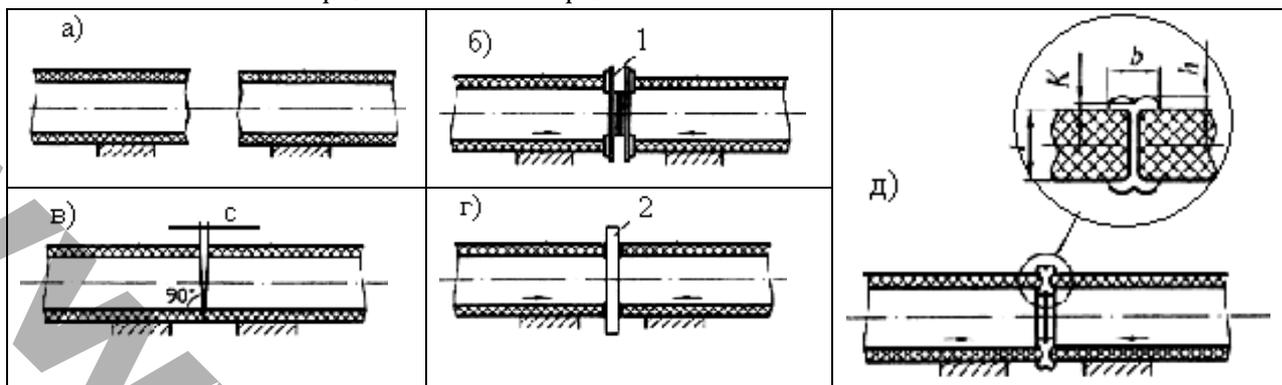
Сварка ПТ2сМ (ПТ2сГ) нагревательным инструментом:
